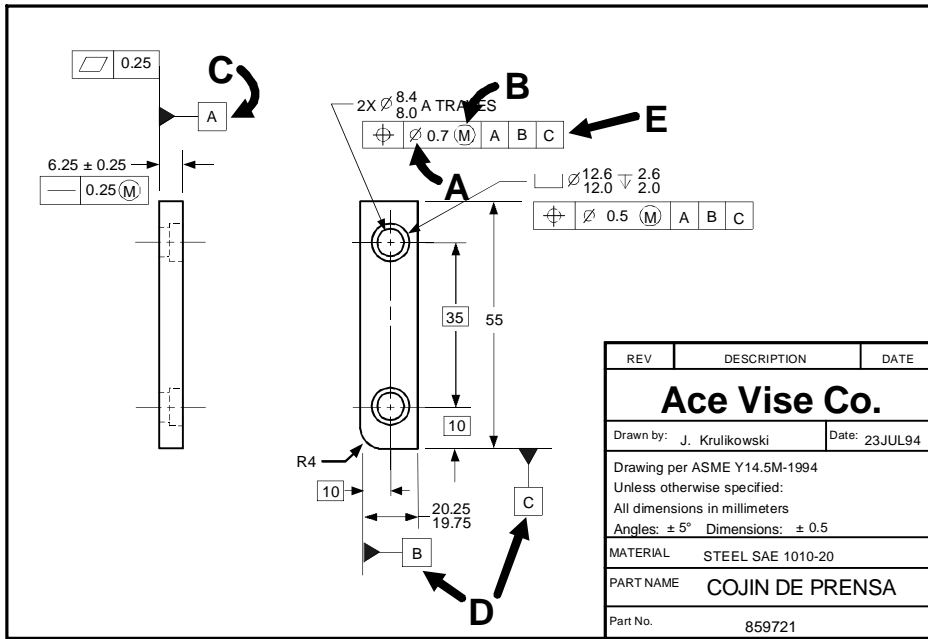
Dibujo de un cojín de prensa usando DTG
